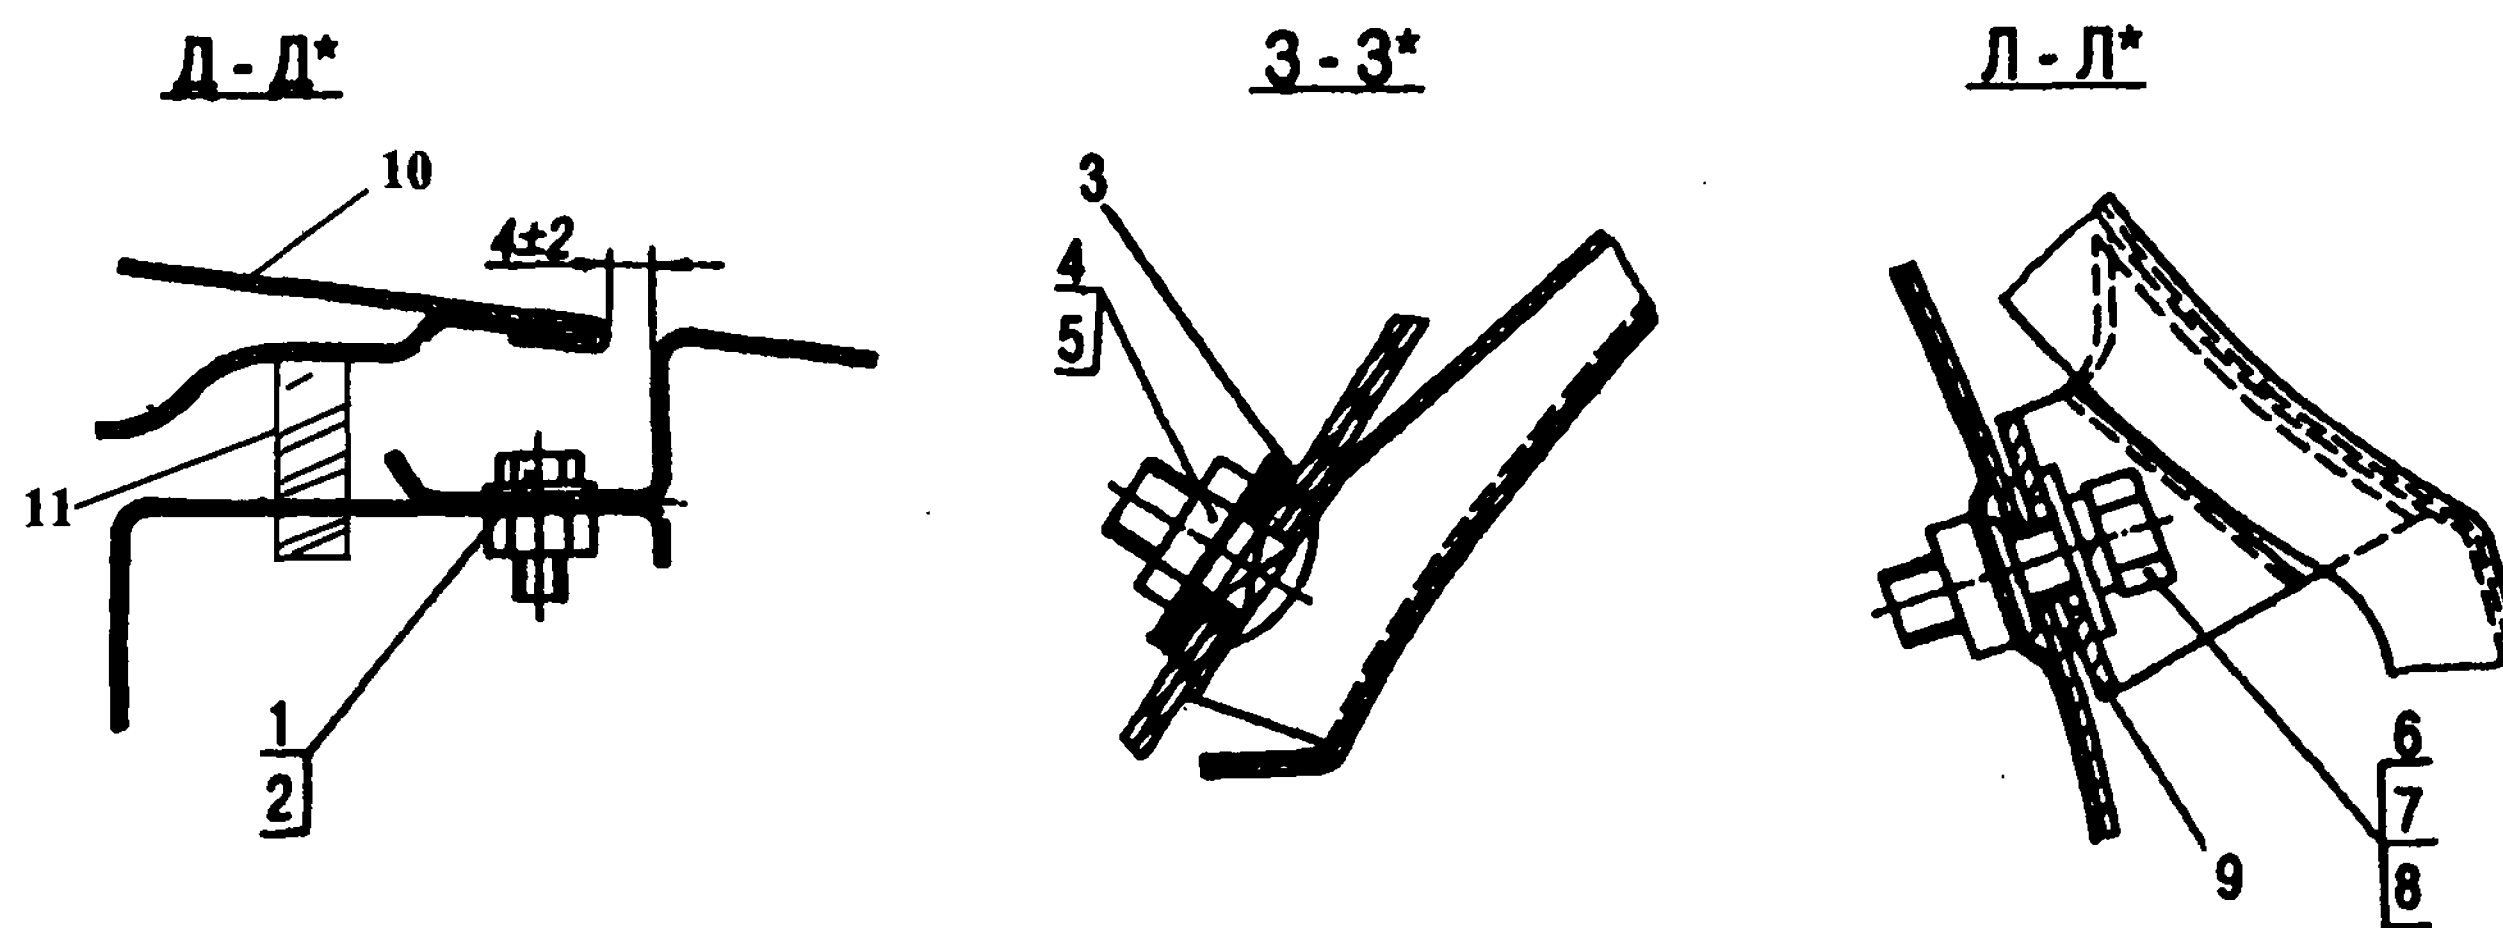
Точки крепления переднего крыла: 1 - болт М6; 2 - шайба; 3 - шайба вибропоглощающая; 4 - гайка М10; 5 - шайба; 6 - болт М10; 7 - шайба пружинная; 8 - шайба; 9 - прокладка дистанционная; 10 - капот; 11 - упор
